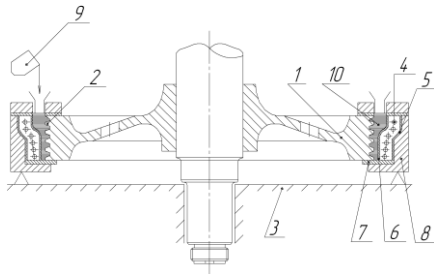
Схема індукційного відновлення циліндричної деталі з симетричними поздовжніми пазами у вигляді різаних пірамід
